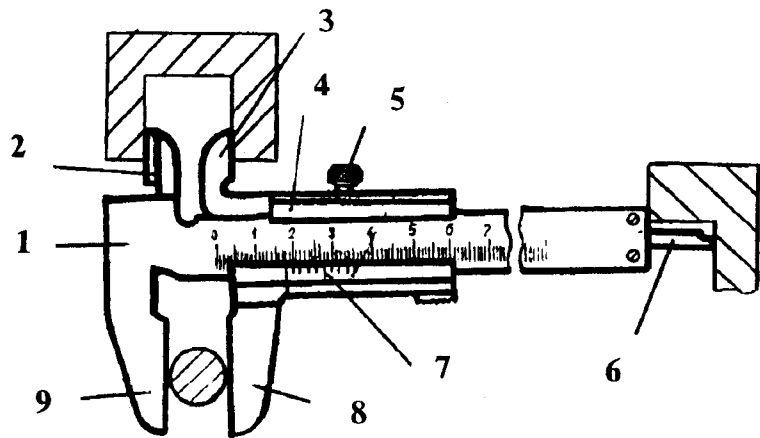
Штангенциркуль ШЦ-1: 1 — штанга; 2 — верхняя неподвижная губка; 3 — верхняя подвижная губка; 4 — подвижная рамка; 5 — зажимной винт рамки; 6 — глубиномер; 7 — нониус; 8 — нижняя подвижная губка; 9 — нижняя неподвижная губка
